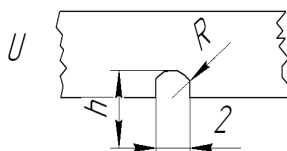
Образец с *U*-образным концентратором для динамических испытаний
